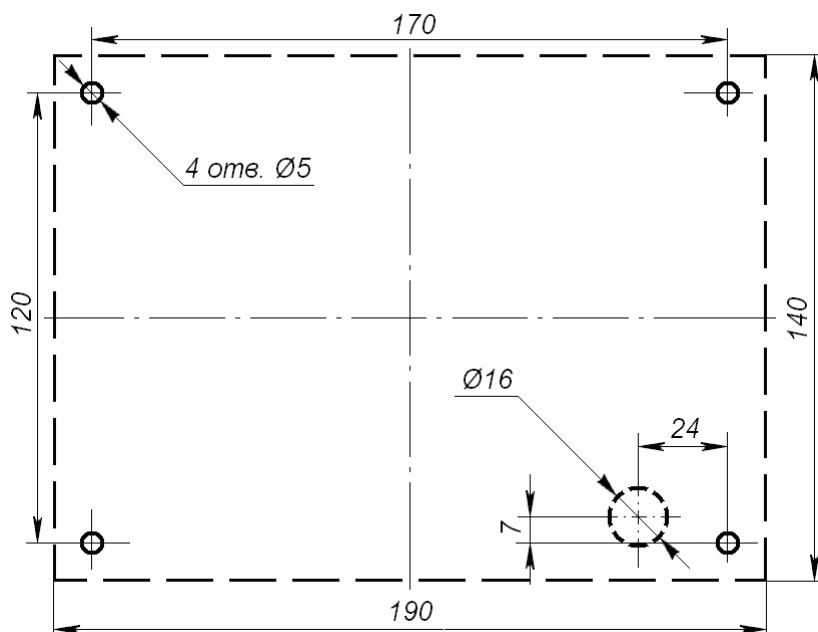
Разметка отверстий для установки контроллера (пунктиром показаны габариты корпуса и место для отверстия под кабели.)
